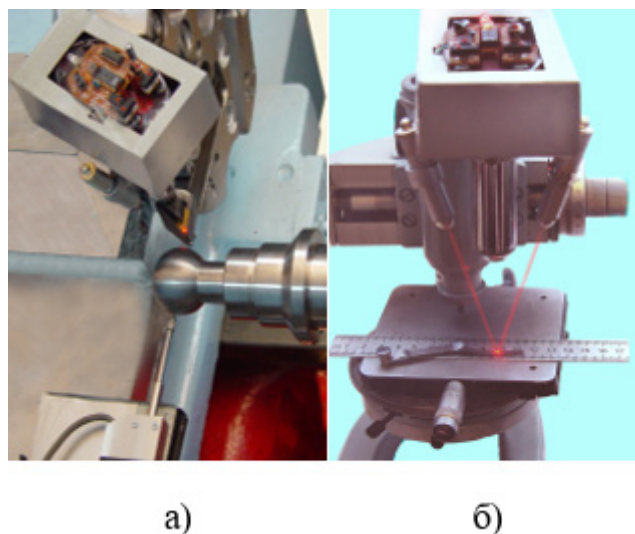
Внешний вид устройств: а) для измерения усадки стружки; б) для калибровки
